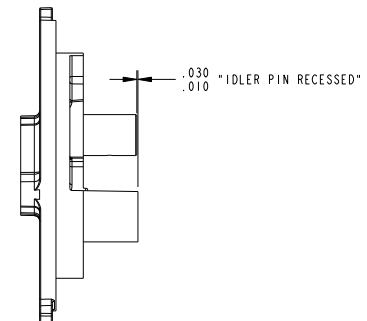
FIGURA J – POSICIÓN DEL PASADOR DE LA POLEA GUÍA
